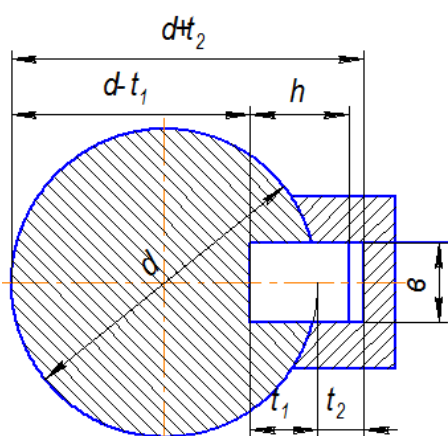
Основные размеры соединения с призматической шпонкой:
